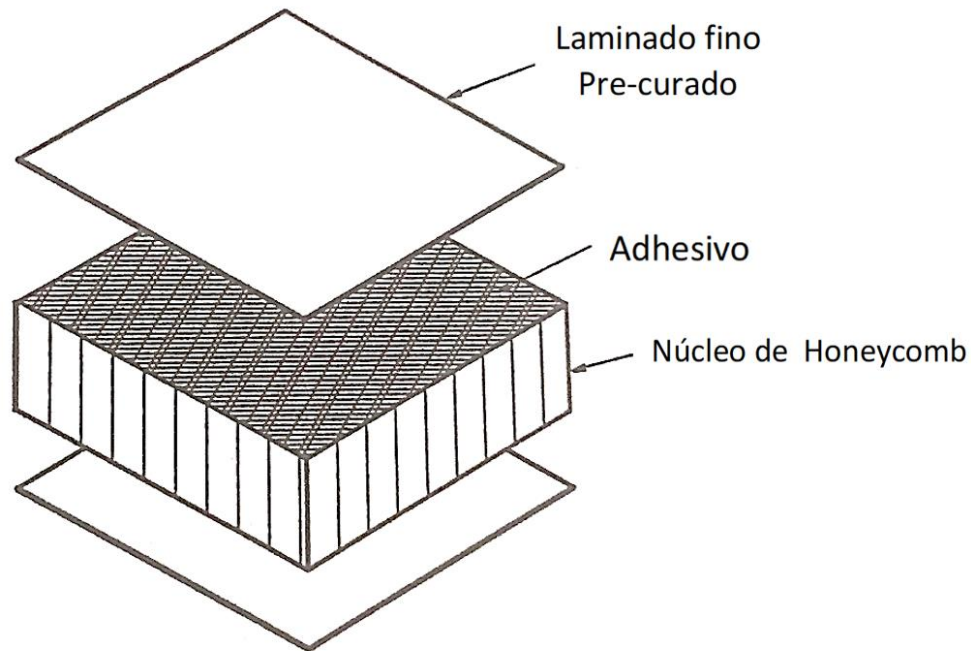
Construcción típica en estructuras tipo sándwich ^[27].
